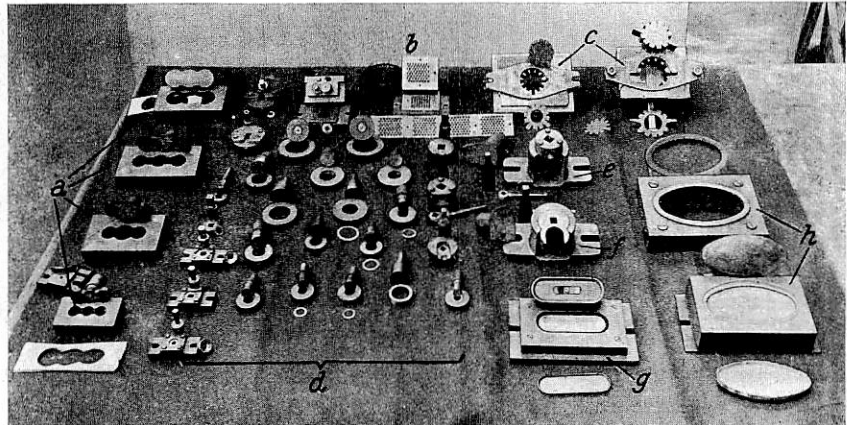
a) Schnittwerkzeuge für Stangenlagerschmiergefäßdichtungen, b) Vorrichtung zum Lochen von Luftsaugeventilsieben, c) Schnitte zur Herstellung der Kolbenschiebersicherungen, d) Schnittzeuge zur Fertigung von Dichtungen, Scheiben u. dergl., e) Werkzeug zum Lochen der vorgebohrten Hahngriffe, f) desgl. für Lappenbolzen, g) vereinigttes Schnitt- und Stanzzeug für Achslagerschmierdeckel, h) Schnitt- und Stanzzeug für die Böden der Wasserkastenschwimmer.
